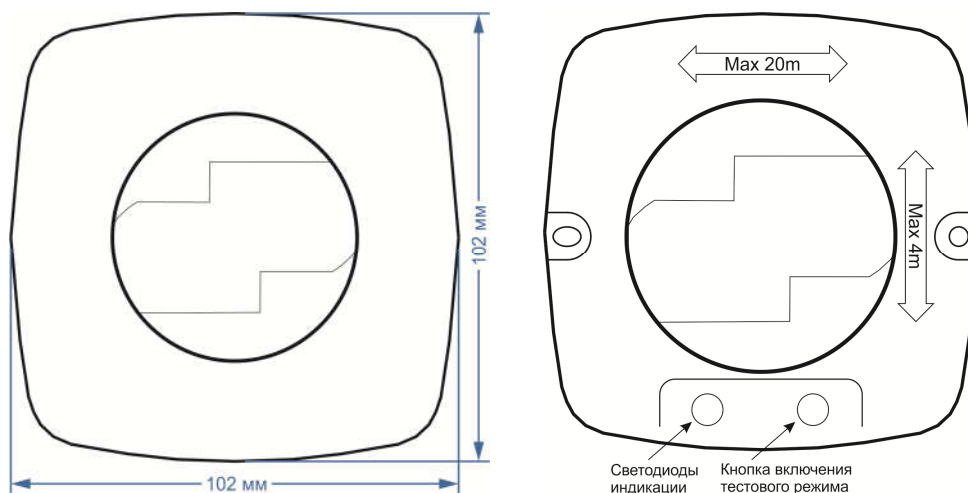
Внешний вид датчика. Габаритные размеры при установленной крышке (слева).
